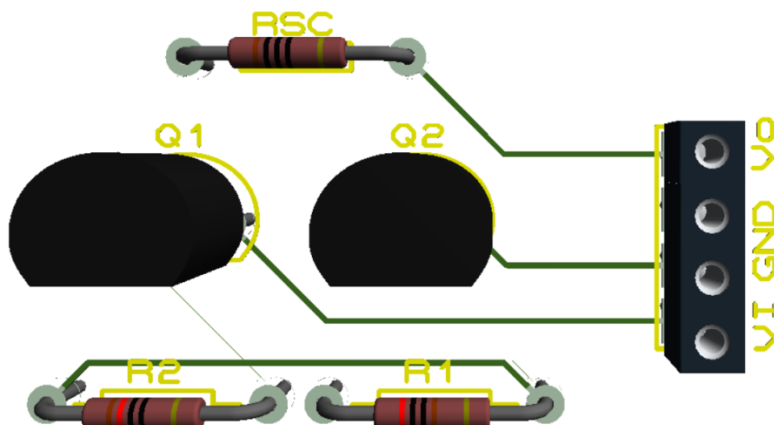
Diseño PCB del circuito de protección contra sobrecarga
